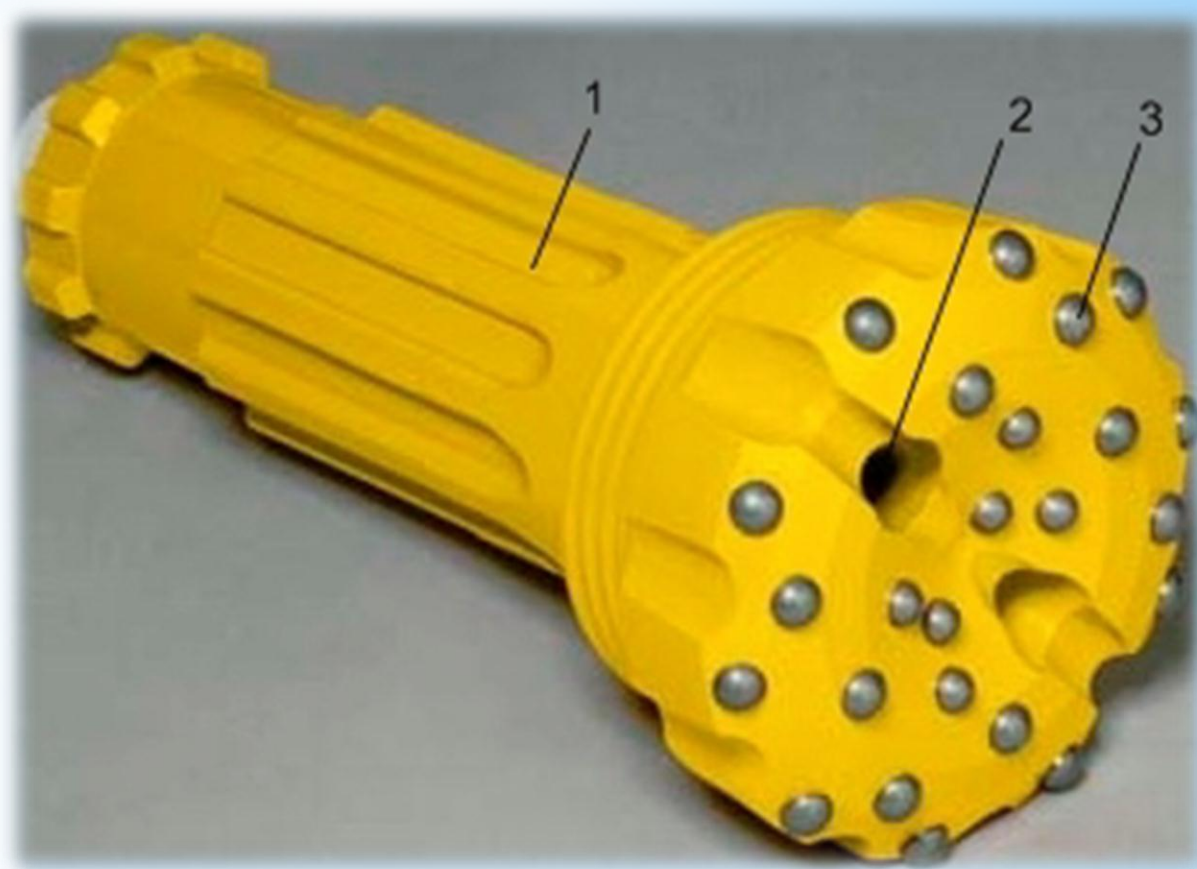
Породоруйнівна коронка заглибного пневмоударника: 1 - корпус; 2 - канали для продувки; 3 - твердосплавні вставки
